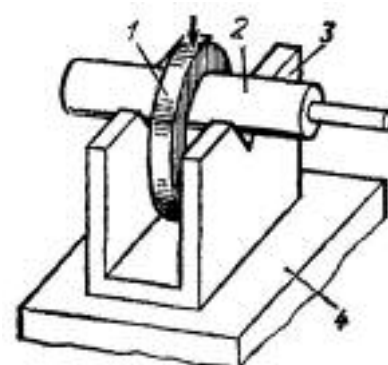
Раскатка заготовки в виде кольца на молотах
